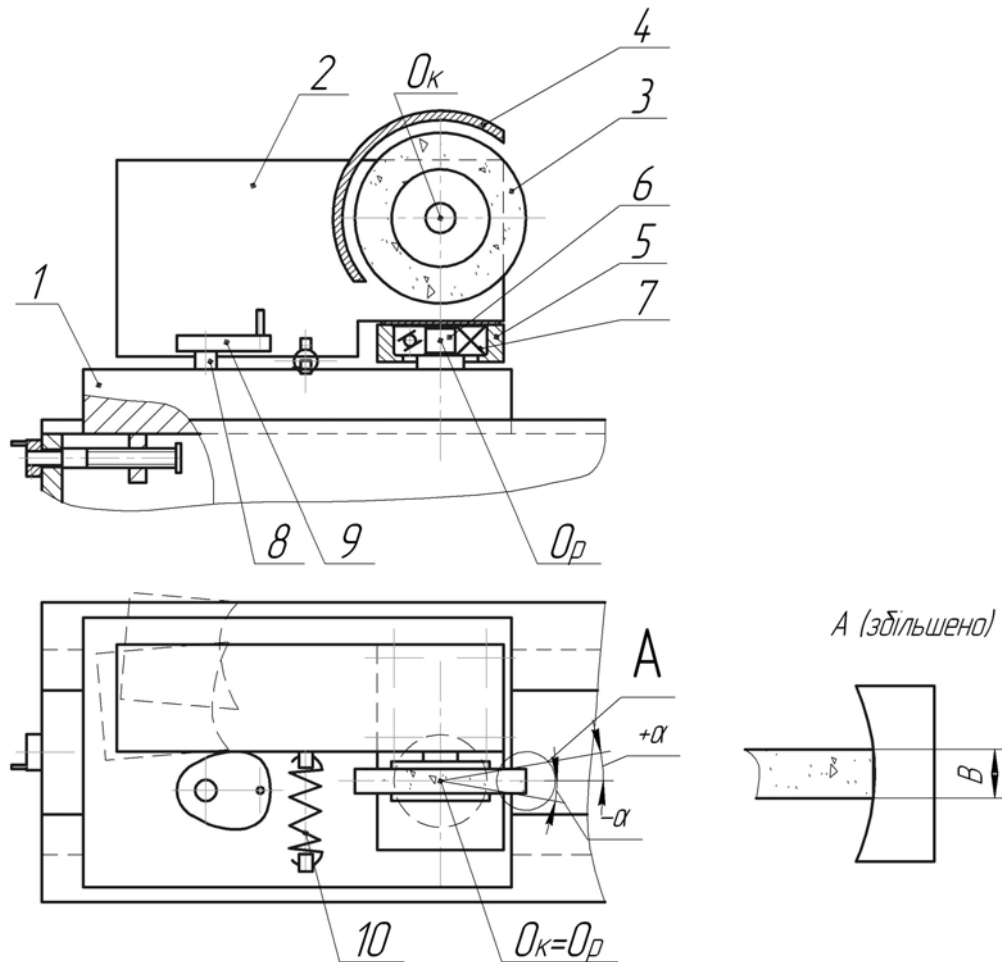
Принципова схема пристрою для шліфування сферичних поверхонь
